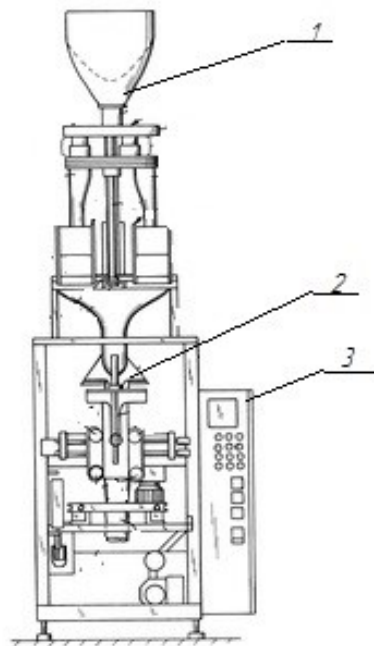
Загальний вид : 1-бункер; 2- рукавоутворювач; 3- блок керування
